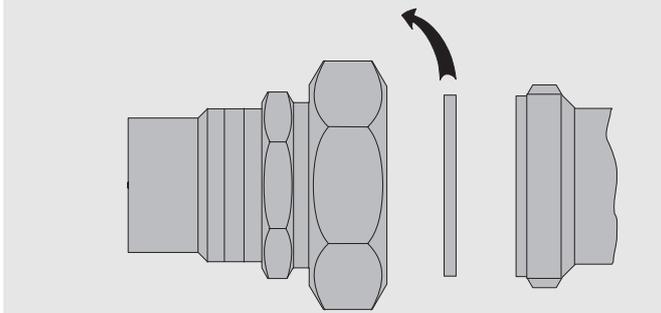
Rohrverschraubung mit Verschluss-Scheibe
